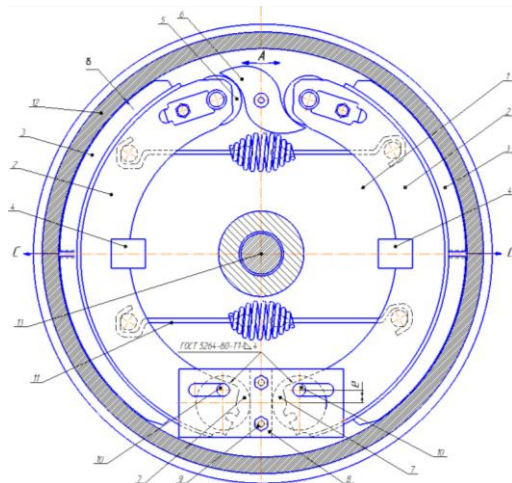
Кинематическая схема тормозного механизма: А – усилие разжимного кулака; δ – зазор; е – эксцентриситет; С – перемещение тормозных колодок; 1 -опорный диск; 2 – тормозная колодка; 3 – тормозная накладка; 4 – скоба; 5 – ролик; 6 –разжимной кулак; 7 – эксцентрик; 8 –упорная площадка; 9– болт; 10 – ось эксцентрика; 11 – пружина; 12 – тормозной барабан; 13 – ось вращения
